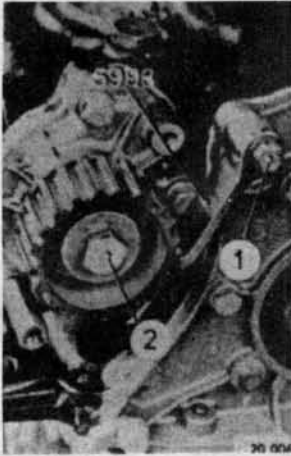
Снятие шестерни привода промежуточного вала
